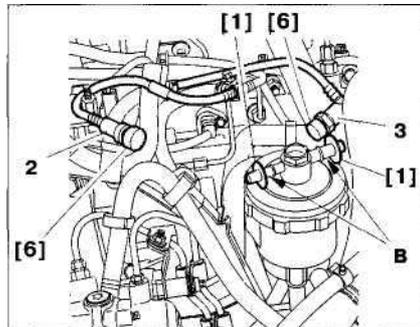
Отсоедините трубки 2 и 3. Дождитесь полного вытекания дизельного топлива. При отсоединении трубок закупорьте их с помощью приспособлений [6], а трубки на топливном фильтре В - с помощью приспособления [1].
